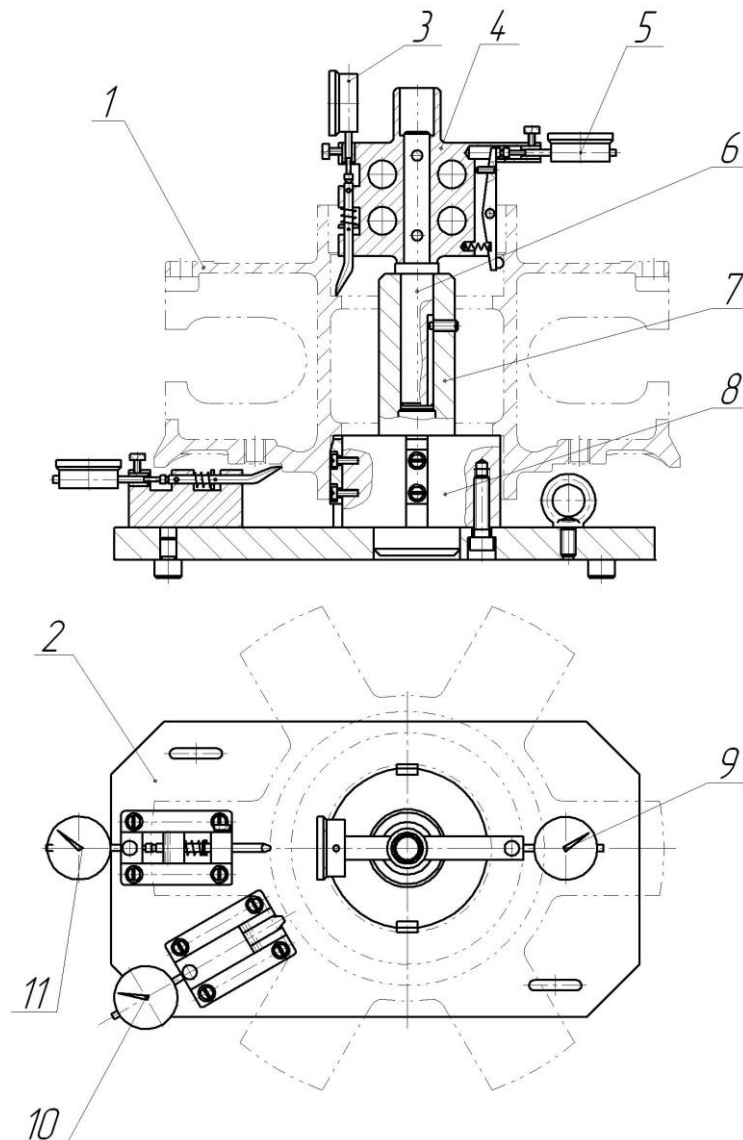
Пристрій контрольний маточини колеса автопричепа 5232:
